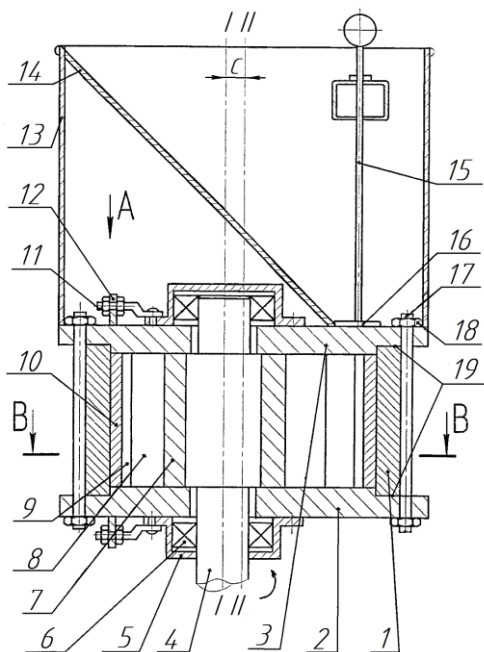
Пресс для брикетирования, вид сбоку в разрезе: 1 – кожух; 2 – нижний фланец; 3 – верхний фланец; 4 – вал; 5 – плита; 6 – подшипник; 7 – формующее колесо; 8 – пластинчатые зубья; 9 – пластинчатые зубья второго формующего колеса; 10 – второе формующее колесо; 11 – регулировочные тяги; 12 – упор; 13 – съёмное загрузочное устройство; 14 – внутренняя конусная поверхность; 15 – рычаг управления заслонкой; 16 – заслонка; 17 – сквозная шпилька; 18 – гайка; 19 – регулировочные прокладки
